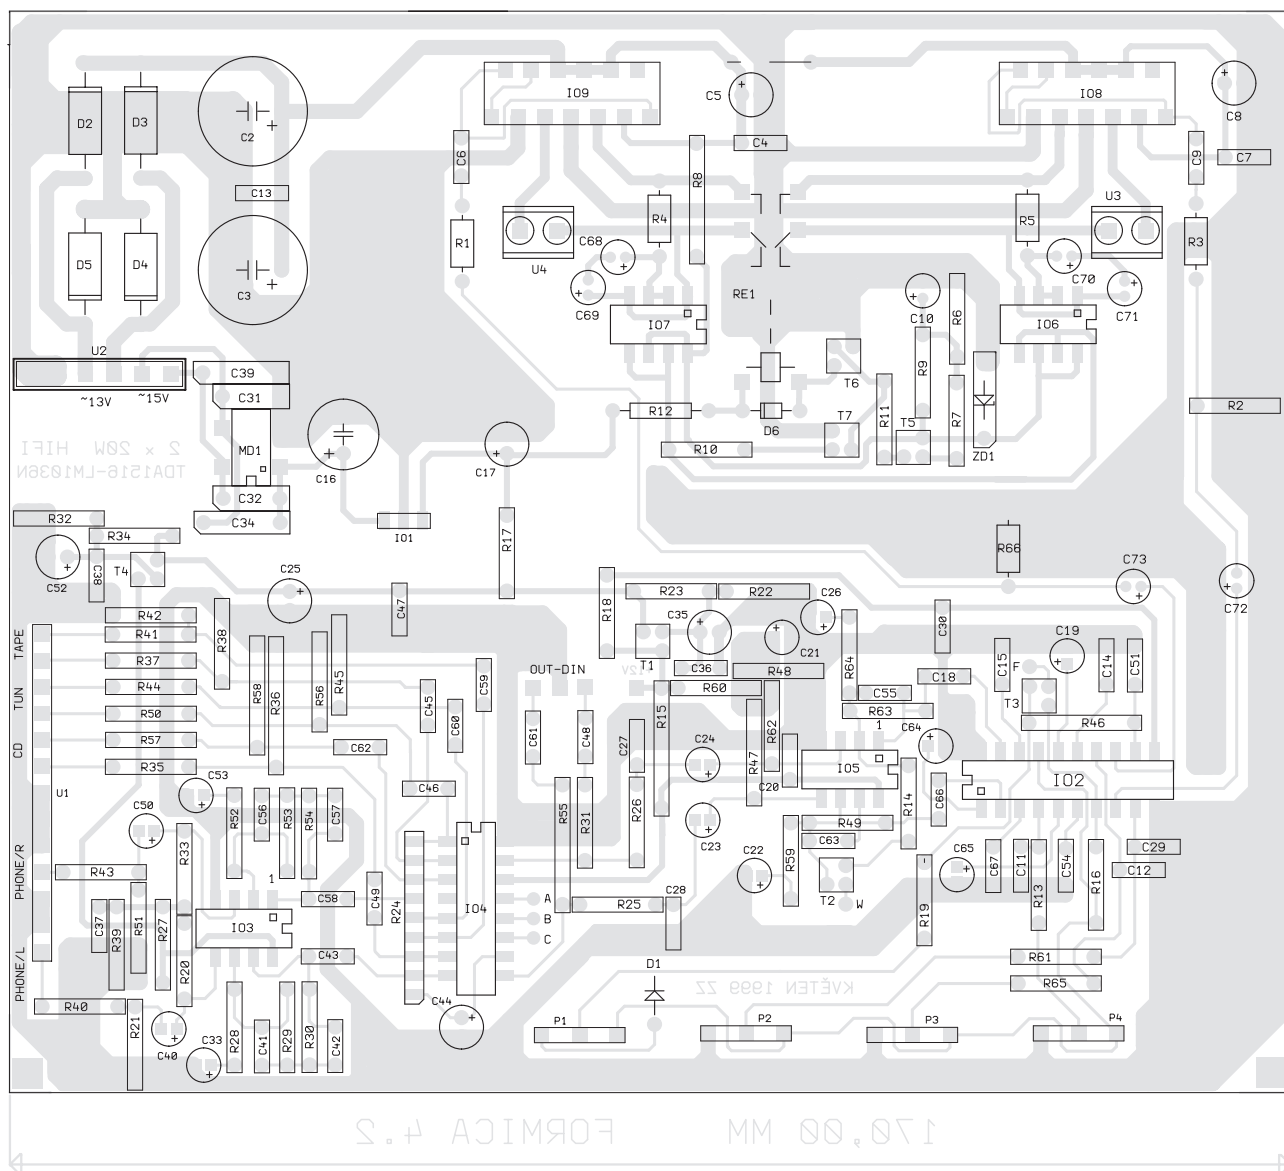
Univerzální deska BOARD-2. Skutečný rozměr 100 x 160 mm
